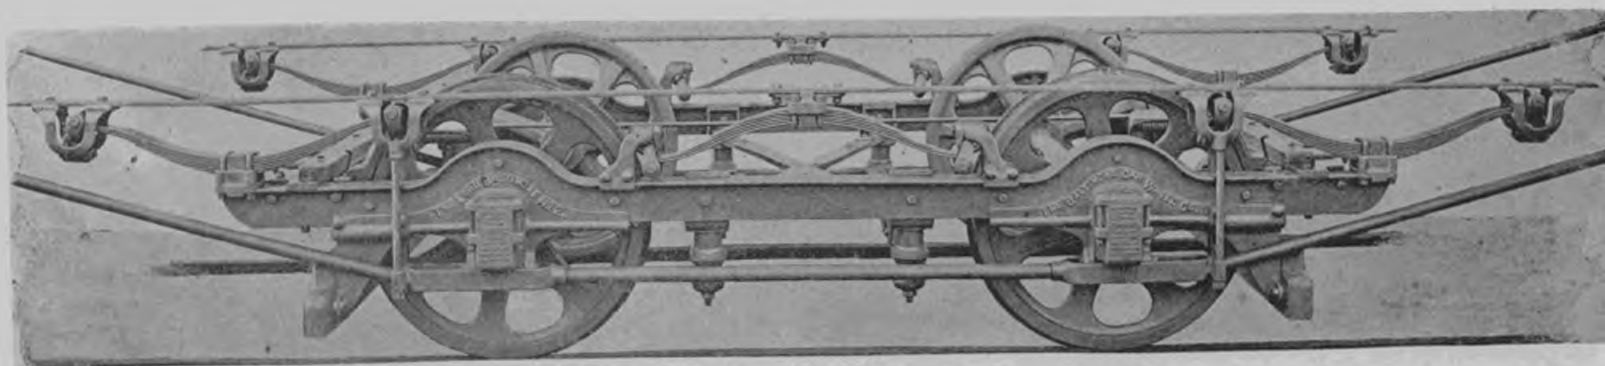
CHASSIS LÉGER DE LA BALTIMORE WHEEL CO
